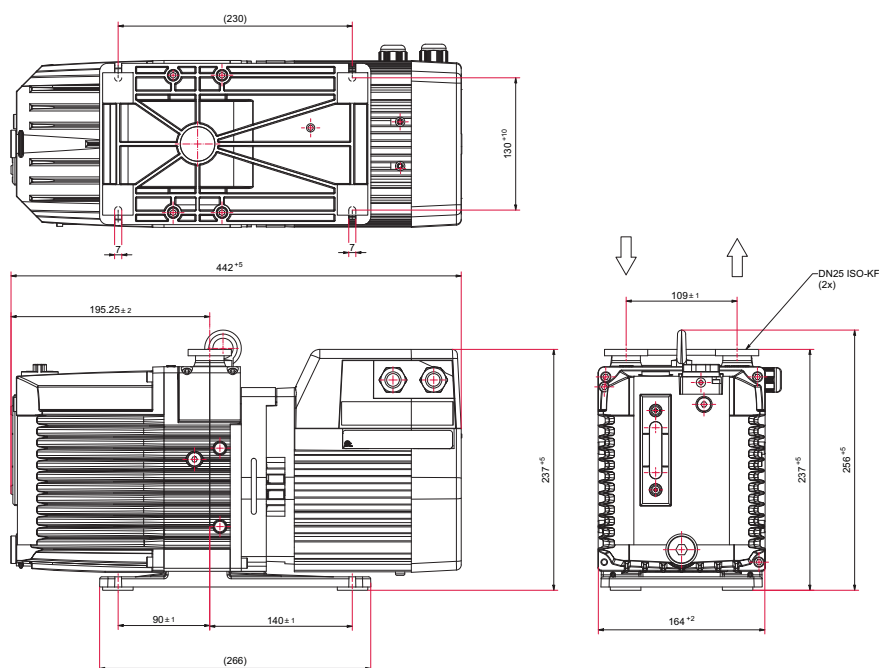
Dimensions DuoVane 18 avec moteur triphasé
